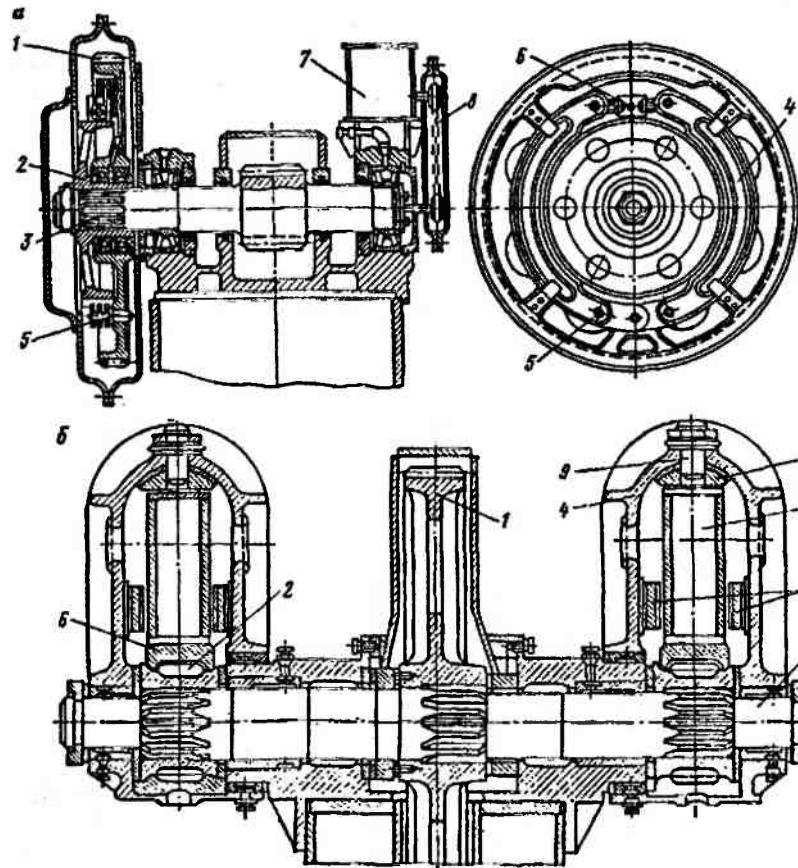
Механизм реечного напора экскаватора ЭКГ-5А:
